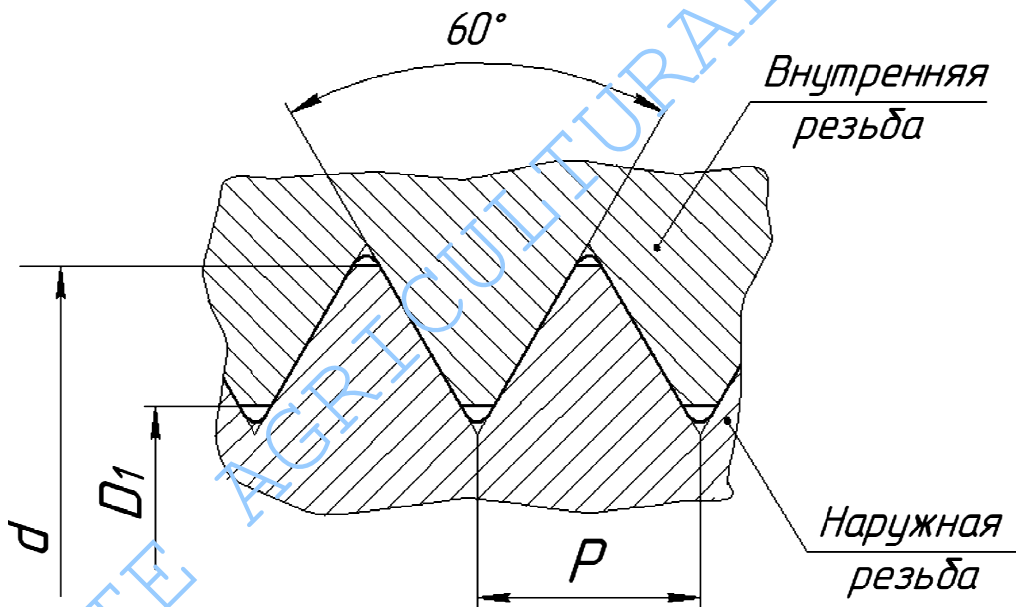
Резьба метрическая (ГОСТ 9150-81)
